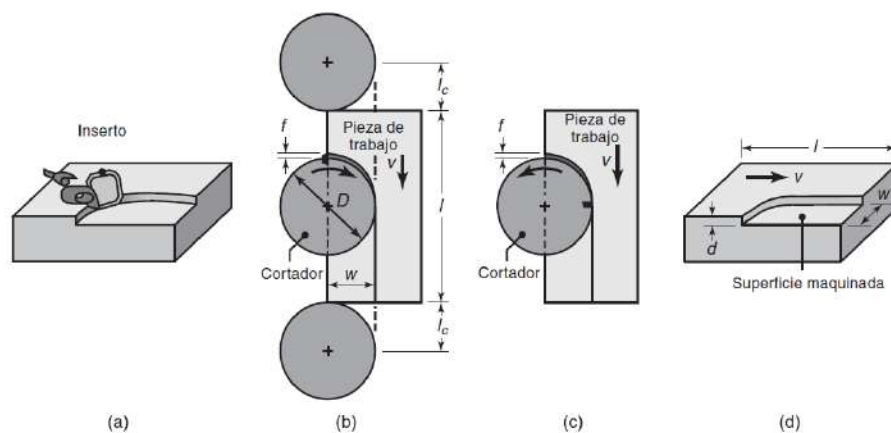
Operación de fresado de careado que muestra a) la acción de un inserto en el fresado de careado; b) fresado concurrente; c) fresado convencional; d) dimensiones en el fresado de careado.
